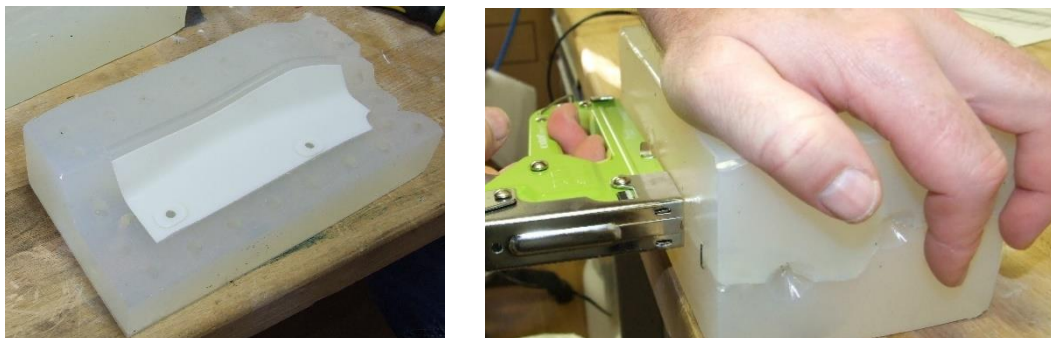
Posunutí v rámu, odlévání druhé poloviny formy
